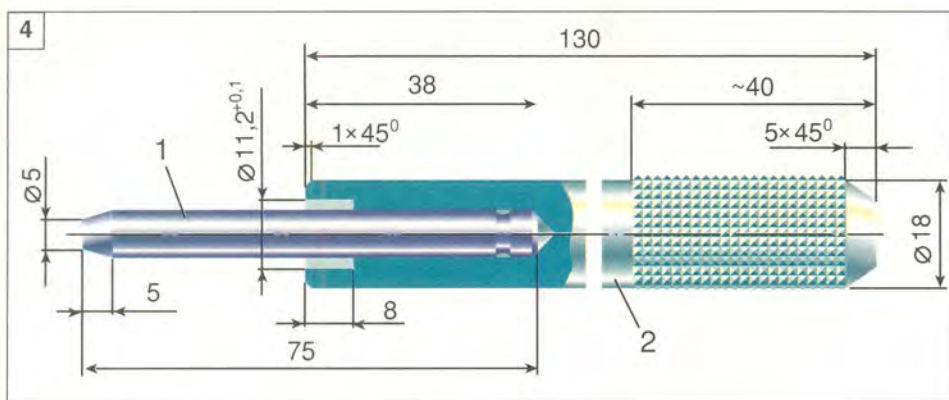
Оправка для запрессовки направляющей втулки клапана двигателя на автомобилях ВАЗ, ЗАЗ: 1 – стержень от изношенного клапана; 2 – оправка.
